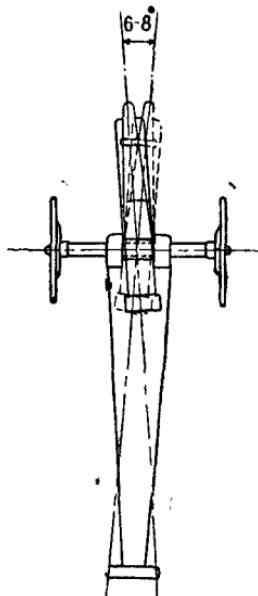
Схема лафета с коробчатым станком. Поворот ствола без перемещения его вдоль боевой оси.
